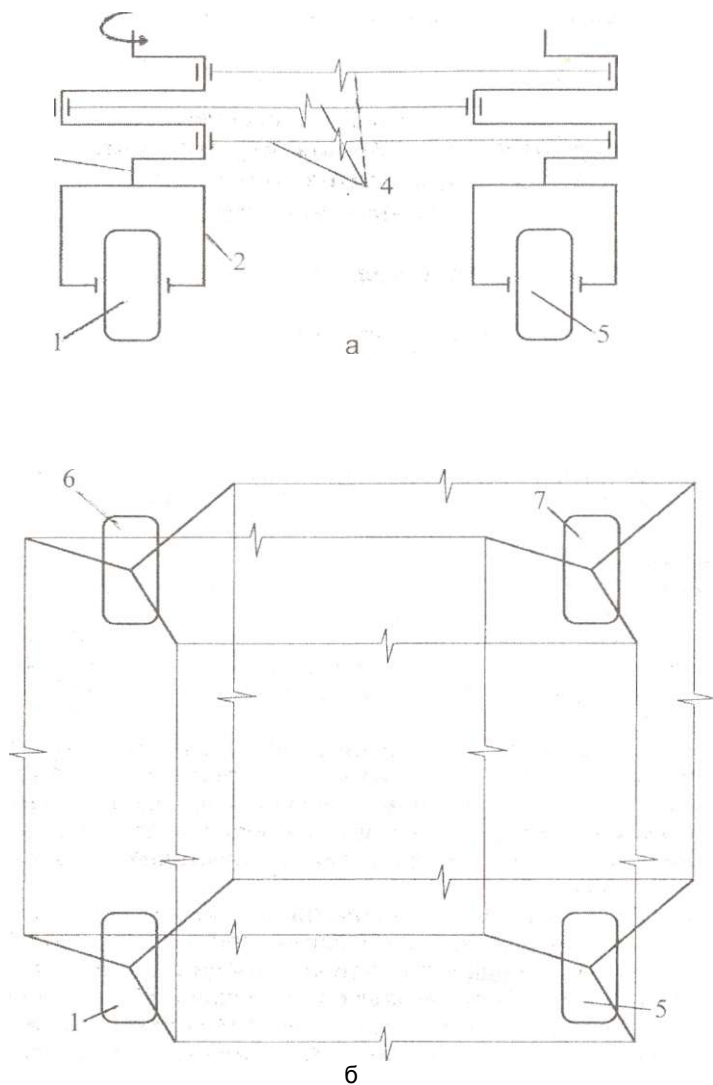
Схема механизма тройного параллелограмма с гибкими связями в многоосной колёсной машине (а - вид спереди, б - вид сверху): 1,5- ведущие мотор-колеса; 2 - вилка; 3 - коленвал; 4 - гибкая связь; 6, 7 - колеса
